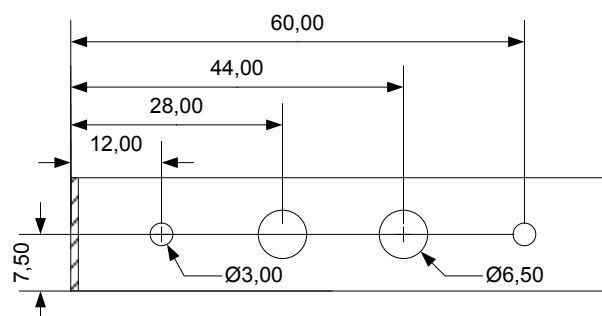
Weißblechgehäuse L-Stück Rückseite
